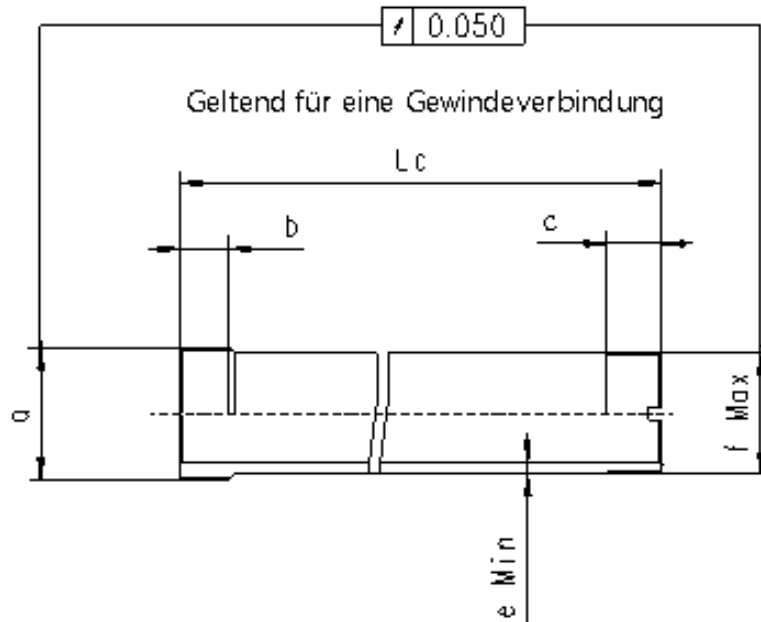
Abmessungen der Zugstange für die Spannfutter
